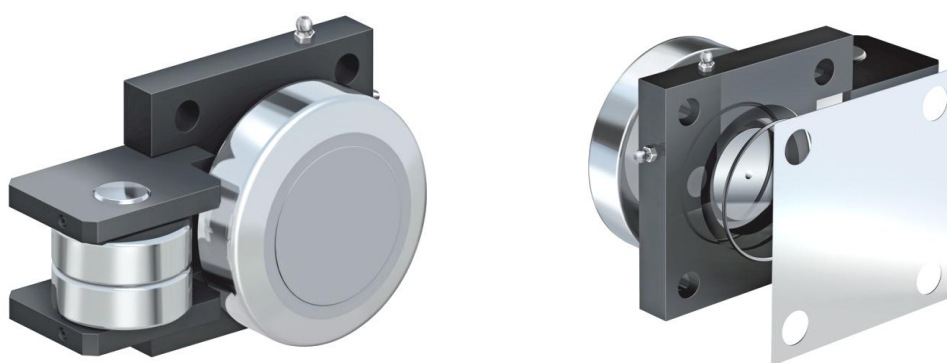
Detail spojení převodovky s posuvným rámem
